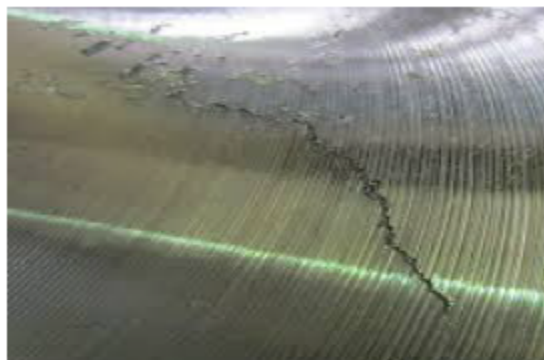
Дефекти поверхні заготовки, що створюють умови переривчатого різання при механічній обробці поверхні
